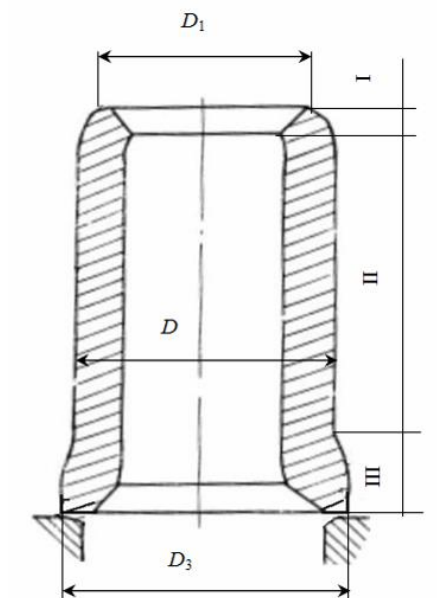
Зміна твірної зовнішньої поверхні заготовки після деформування
